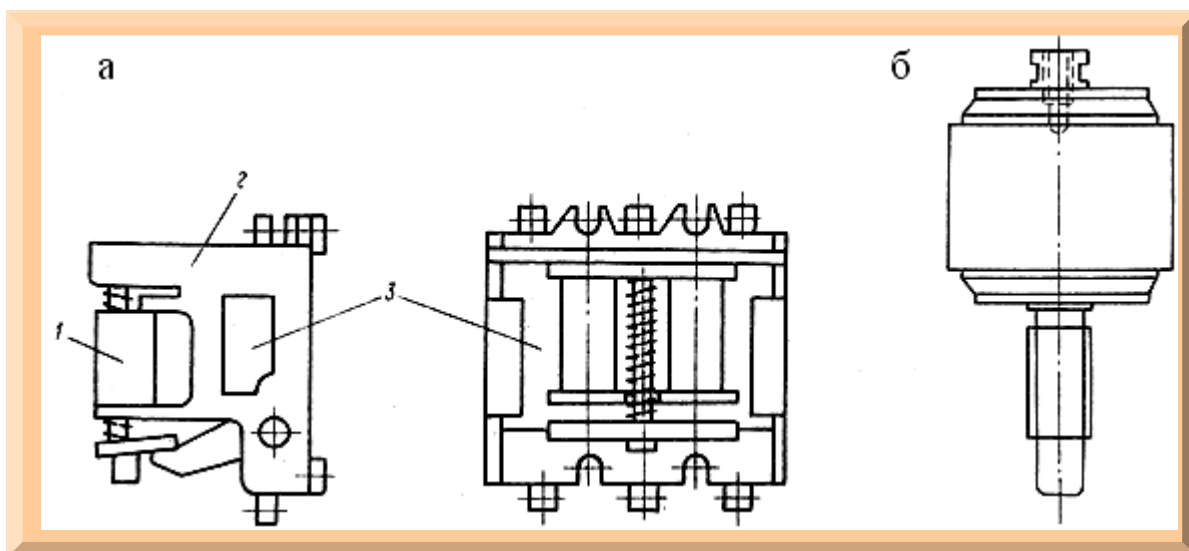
Контакторы переменного тока вакуумные: а - устройство; б - внешний вид
